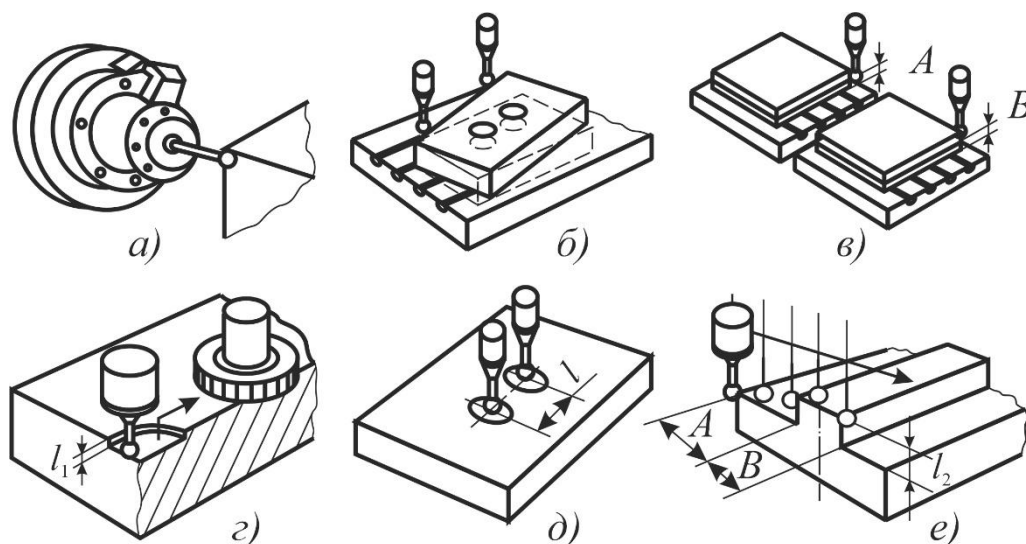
Схемы применения щупов: на сверлильно-фрезерно-расточном станке с ЧПУ для измерения: а – установки нулевой точки; б – погрешности установки заготовки на столе; в – снимаемого припуска; г – припуска на чистовой переход; д – межосевого расстояния; е – обработанной детали
